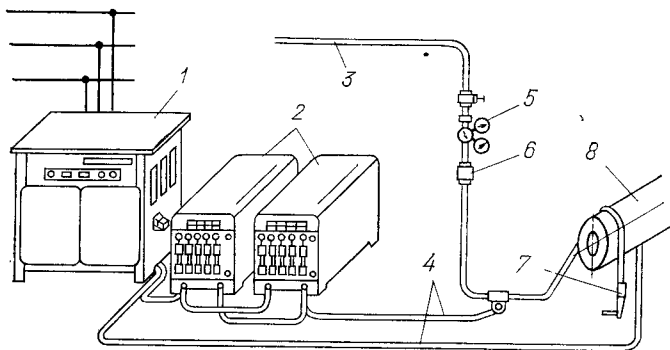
Схема установки для удаления дефектов воздушно-дуговой строжкой: 1 — многопостовый выпрямитель ВКСМ-1000; 2 — балластные реостаты РВ-300; 3 — воздушная магистраль; 4 — сварочные электрические кабели; 5 — воздушный редуктор; 6 — влагоотделитель; 7 — резак; 8 — ремонтируемая деталь.
